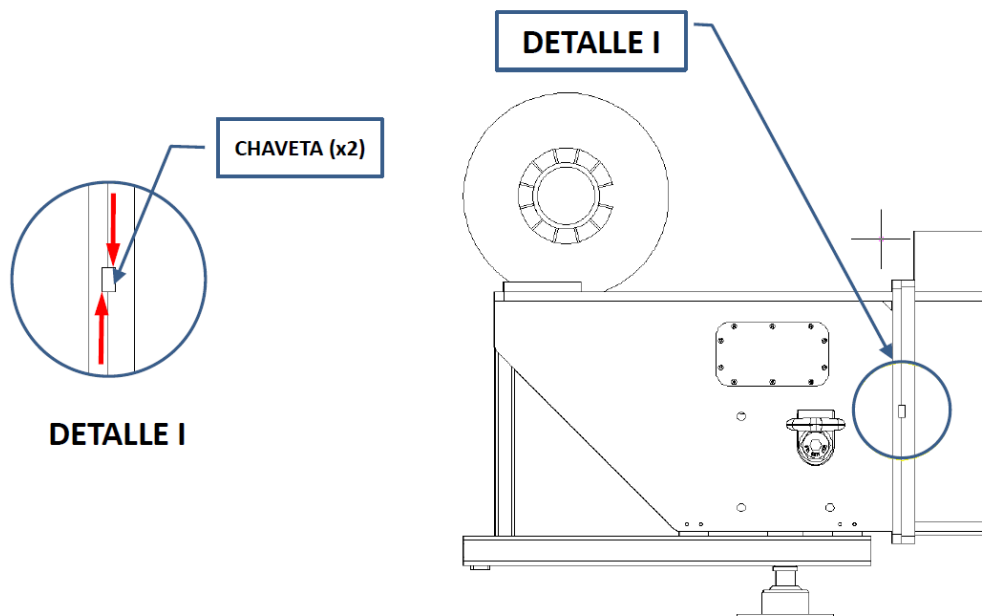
Detalle colocación de las chavetas entre cabeza y viga
